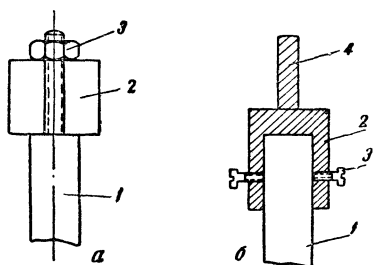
а — крепление насадки на ведущей оси: 1 — ведущая ось; 2 — насадка; 3 — крепящая гайка; б — фигурная насадка: 1 — вал двигателя; 2 — насадка; 3 — стопорные винты; 4 — рабочая часть насадки
